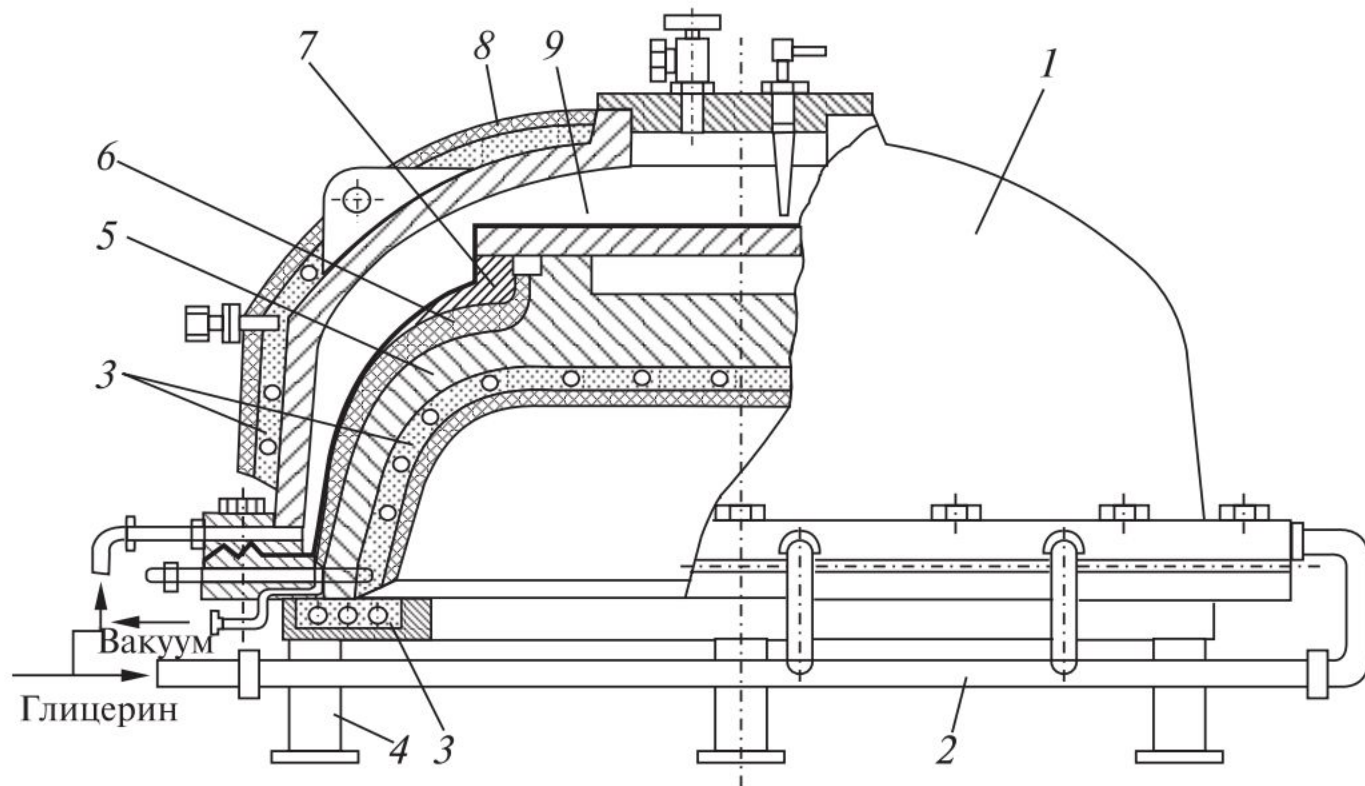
Пресс-форма для изготовления ТЗП днищ корпуса РДТТ.
